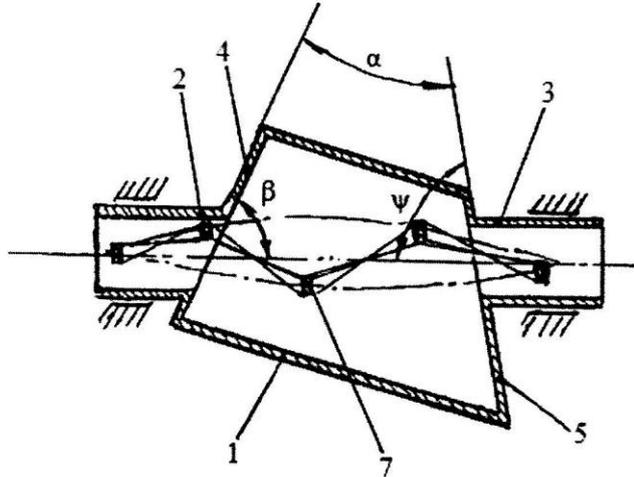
Станок для отделочно-зачистной и упрочняющей обработки деталей на базе комбинированного ротора с винтовой пружиной выпуклой формы:
